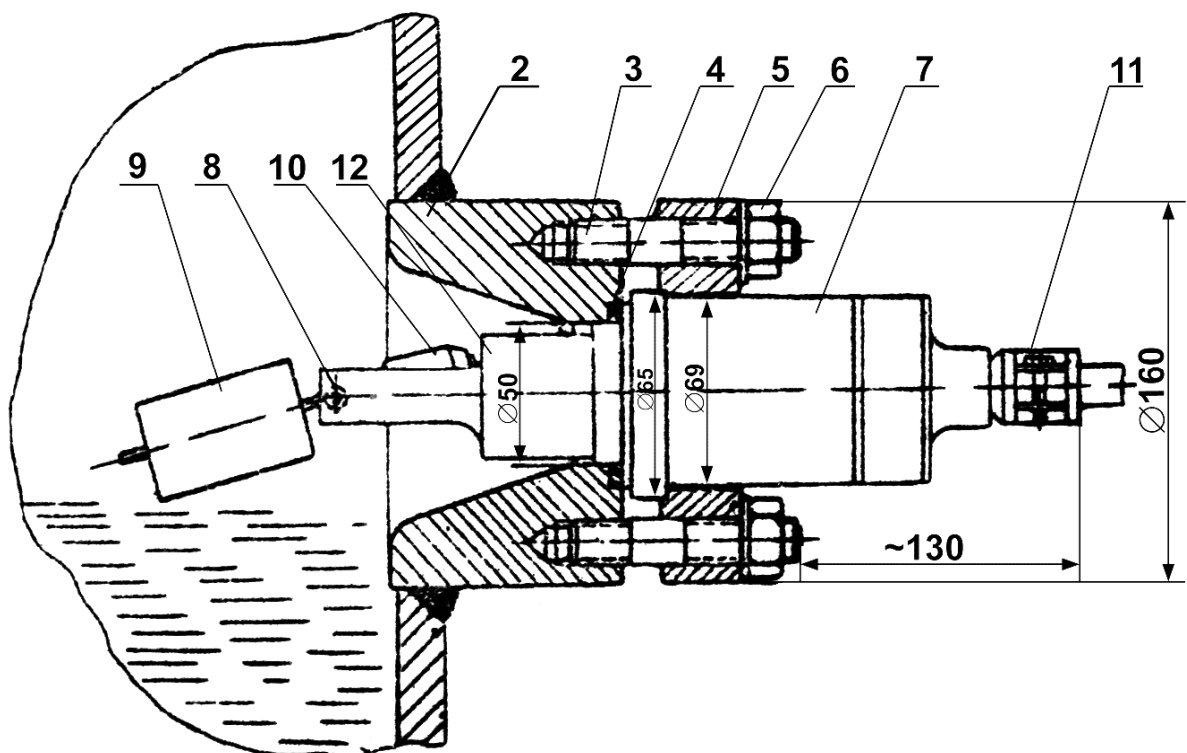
Загальний вигляд і варіант штуцерного монтажу сигналізатора: 1 – апарат; 2 – штуцер; 3 – шпилька; 4 – прокладка; 5 – фланець; 6 – гайка; 7 – втулка сигналізатора; 8 – вісь; 9 – поплавок; 10 – утримувач з магнітом; 11 – з'єднувальний увід; 12 – корпус.
